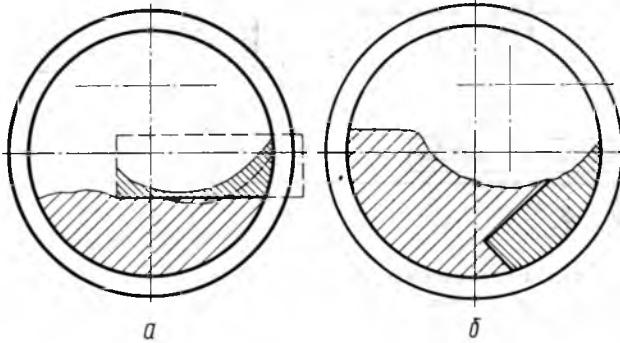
Первоначальная (а) и измененная (б) схема размещения пластинки твердого сплава в корпусе концевой фрезы (разрез)
